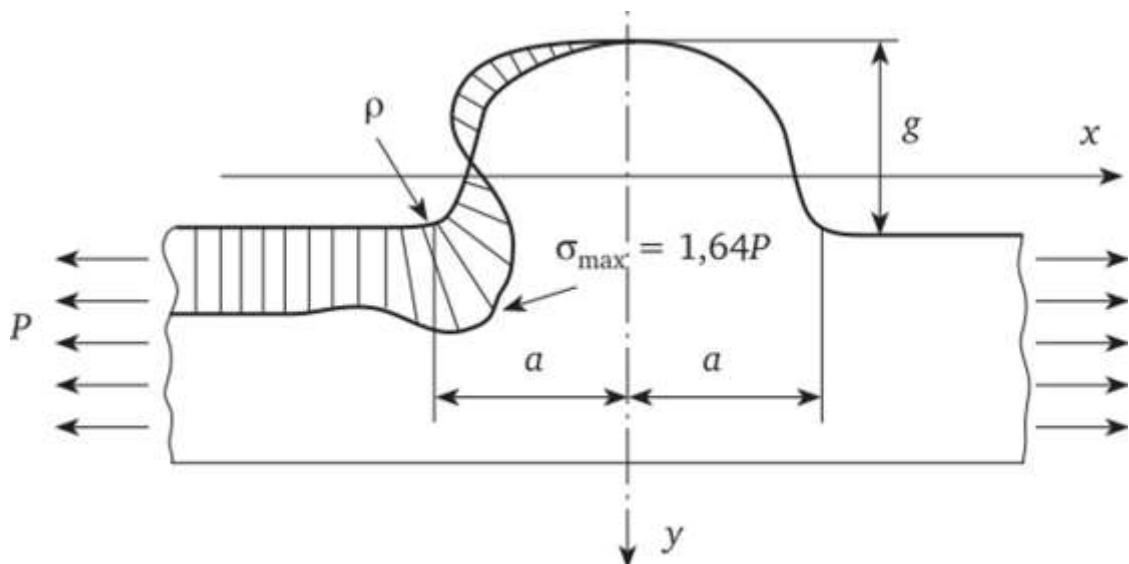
Розрахункова схема зварного з'єднання для визначення концентрації напружень, що викликана зміною перерізу з'єднання
